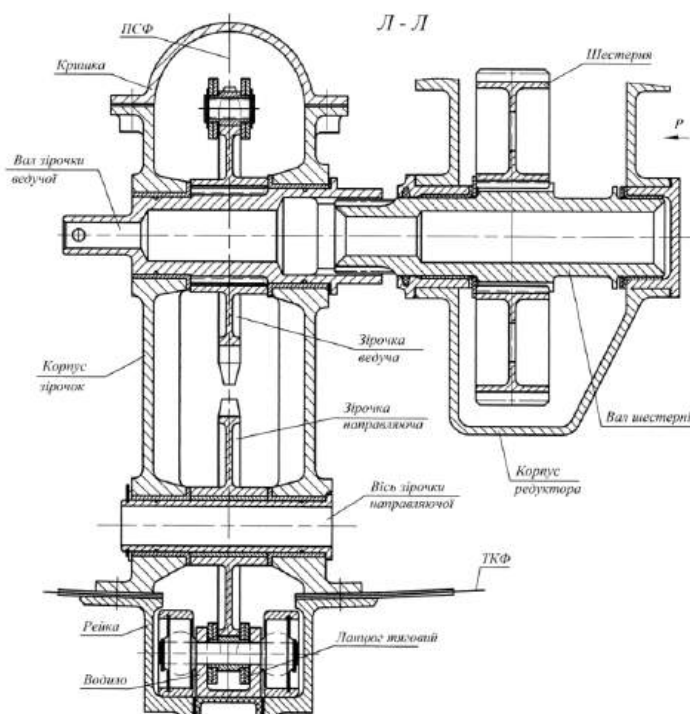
Схема перерізу приводних зірочок, каретки та редуктору приводного механізму
